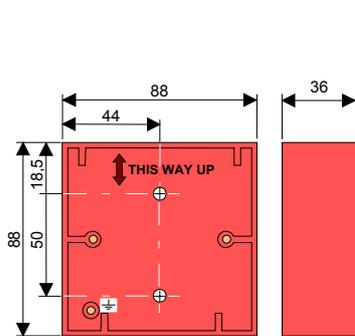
Boîtier pour montage en saillie (Réf. 704980)
